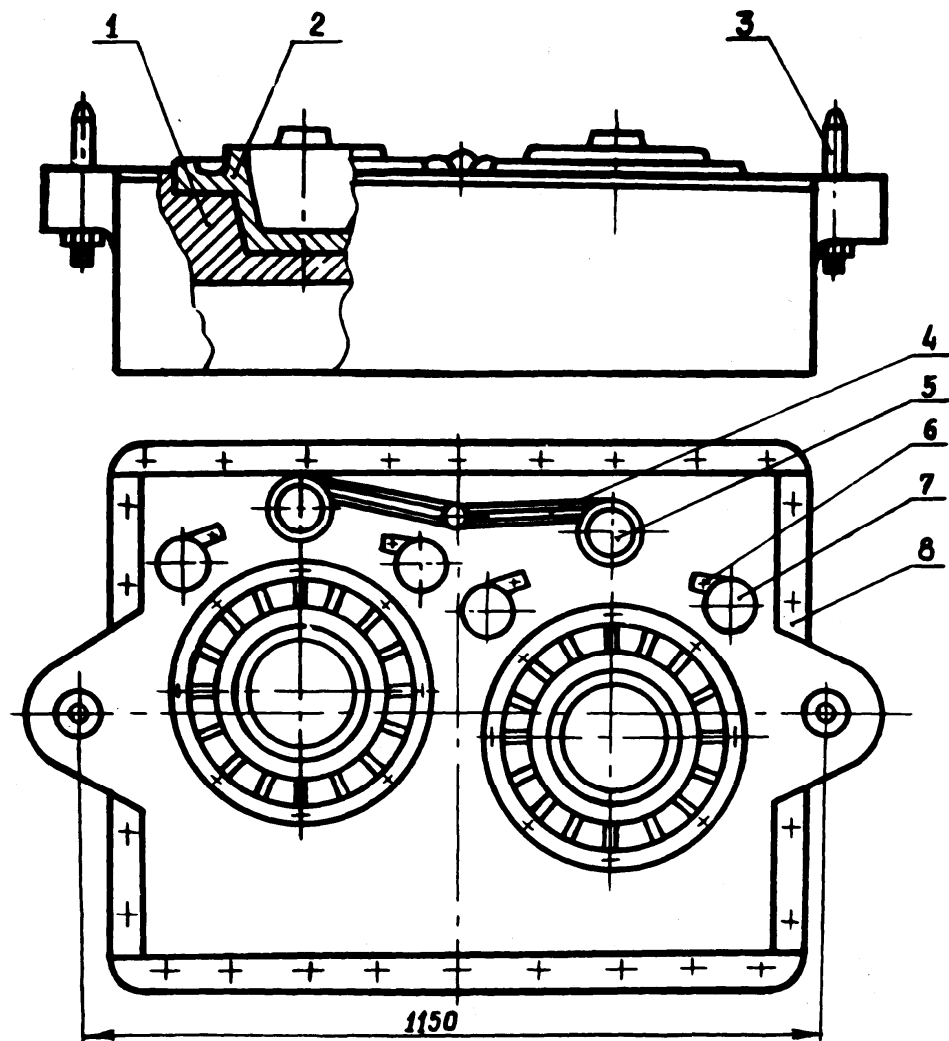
Модельна плита «низу» для виготовлення виливка «Картер планетарного редуктора»: 1 – підмодельна плита; 2- модель виливка; 3 – направляючий штир; 4,6 – моделі ливникових ходів; 5 – модель реакційної камери; 7 – модель прибутку; 8 – захисна броня.
